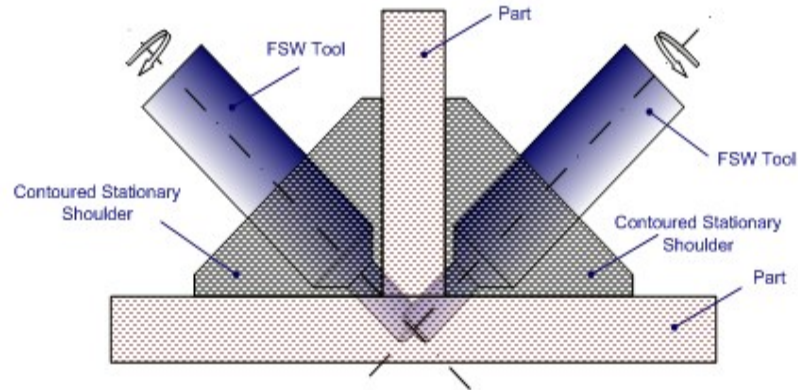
Schéma de la technique appliquée à une configuration soudure [29]
